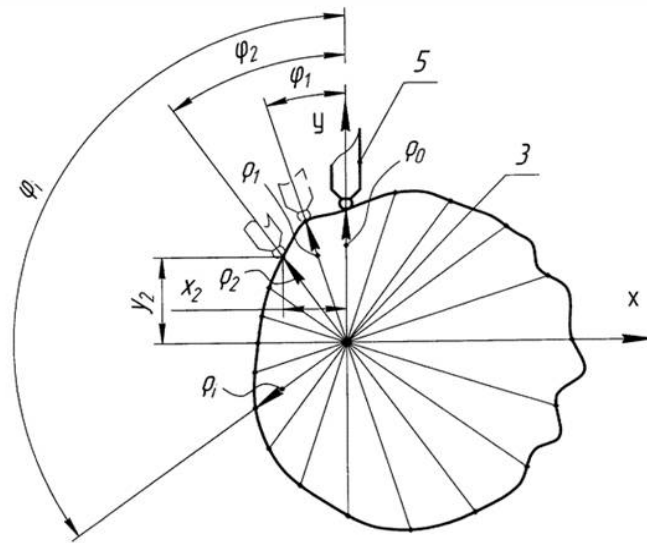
Схема контролю перетину вимірюваної поверхні деталі
